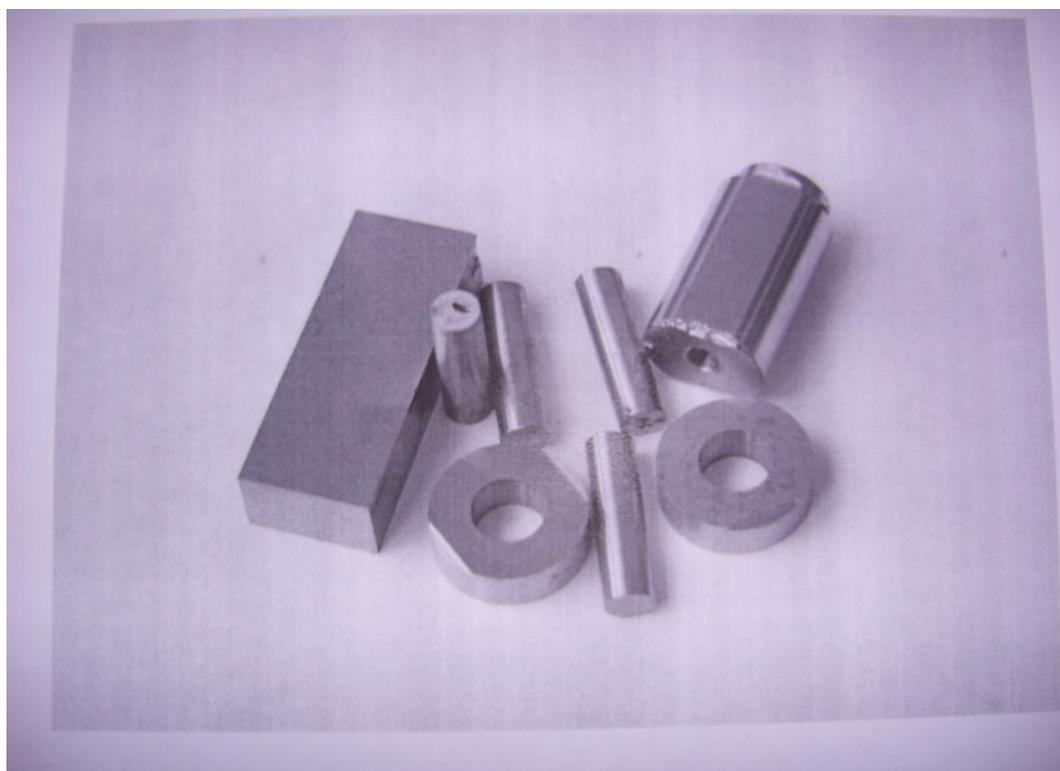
Металлические отходы 1 группы: брак отливок, выявленный на стадии механической обработки и испытаний
